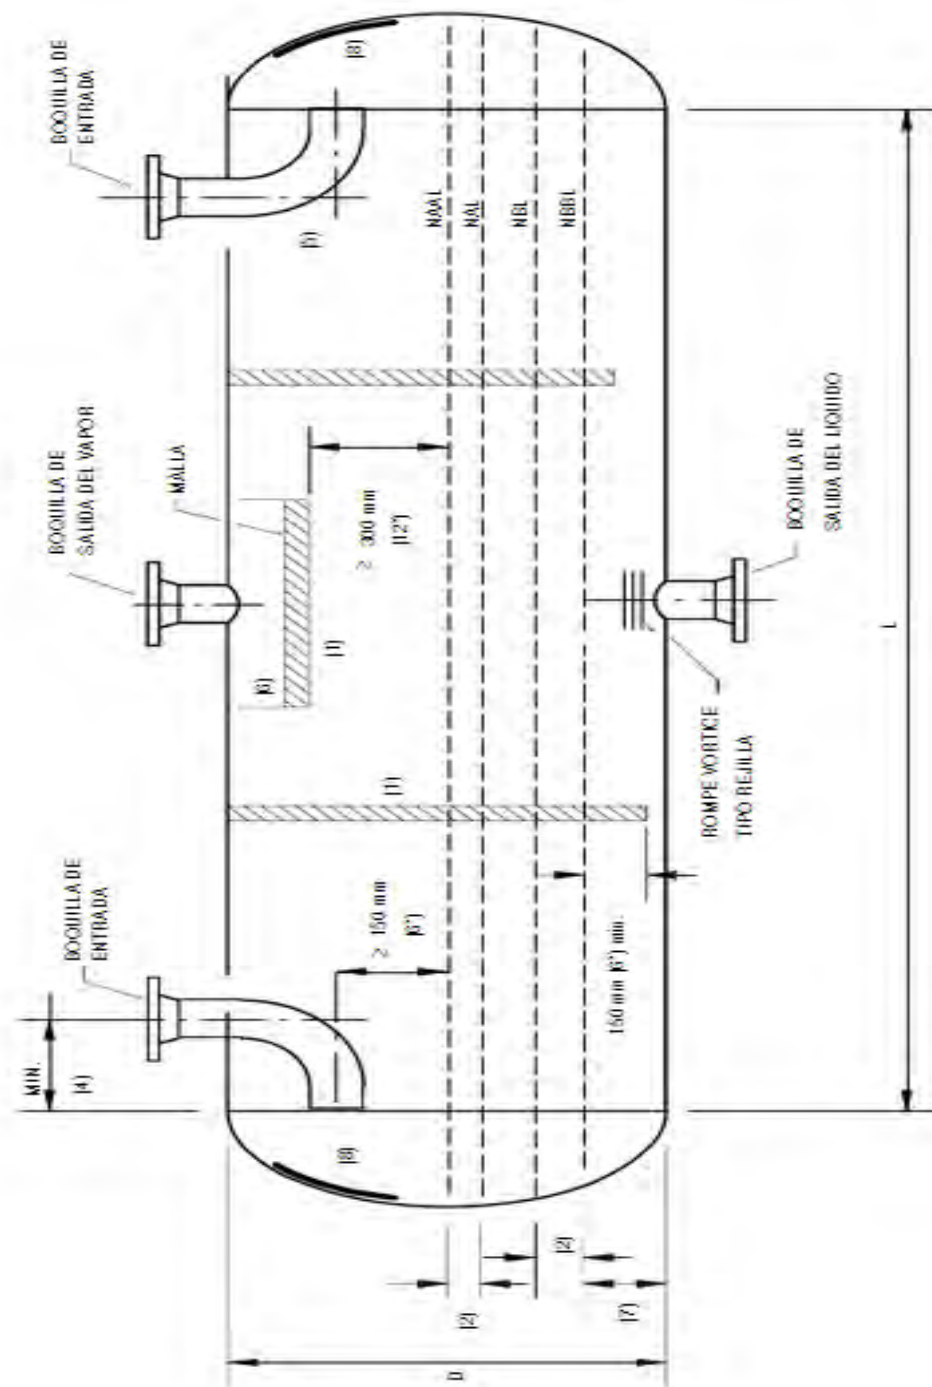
Dimensiones de tambores horizontales con malla vertical y horizontal [8]
